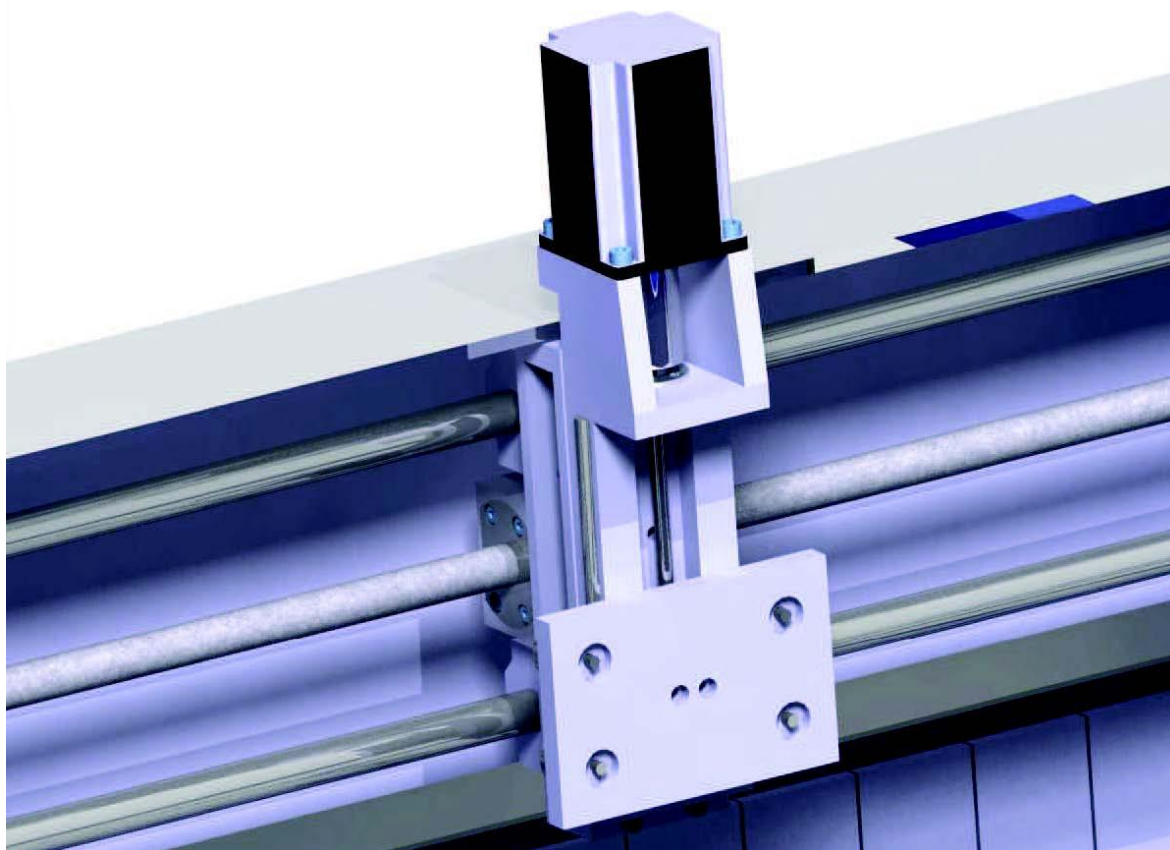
Krokový motor 86HS45 a spojka LK25C
